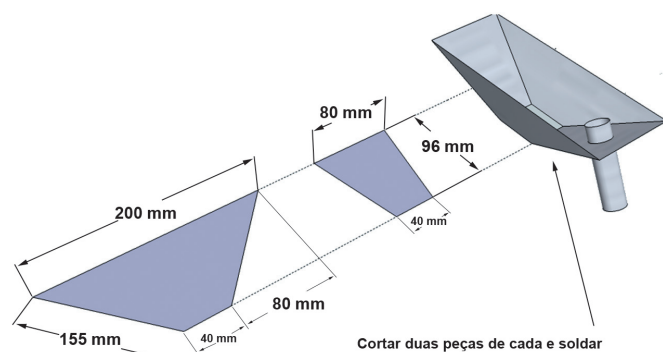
B. Cortes das chapas, dobras e montagem e aspecto final do separador de cerejas.
